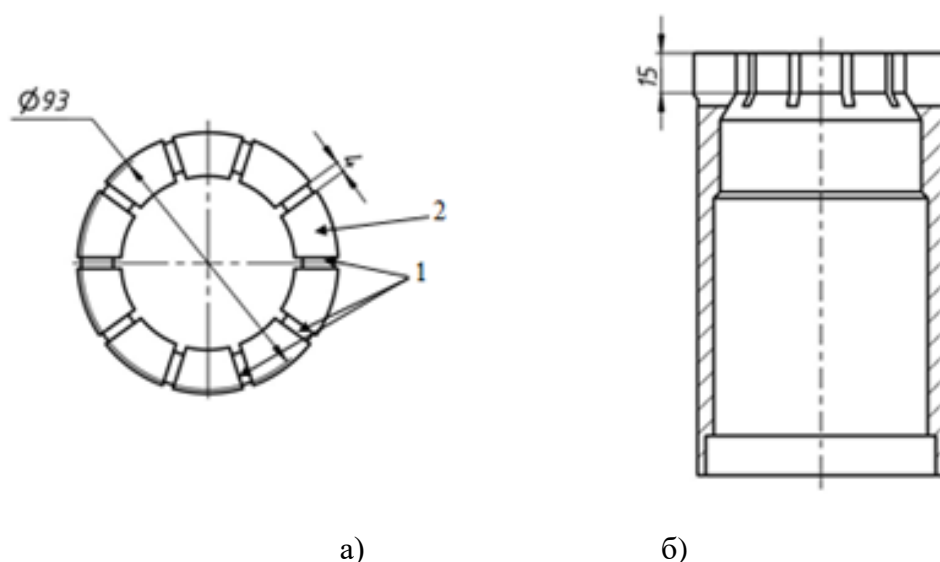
Схема коронки со стандартной формой матрицы: а – вид сверху; б – вид сбоку.
